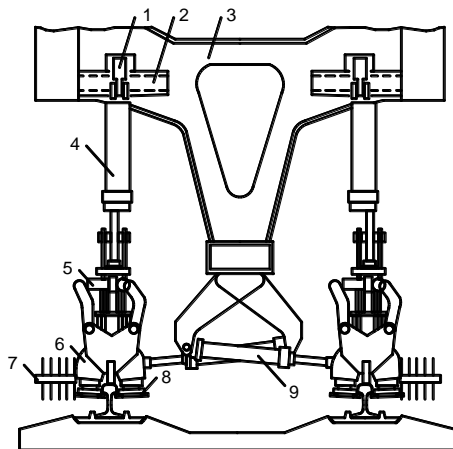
Конструктивная схема подъемно-рихтовочного устройства машины ВПР-02:
